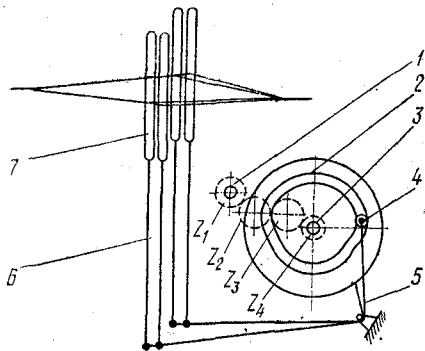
Схема эксцентрикового зверообразовательного механизма ЭР6-2
